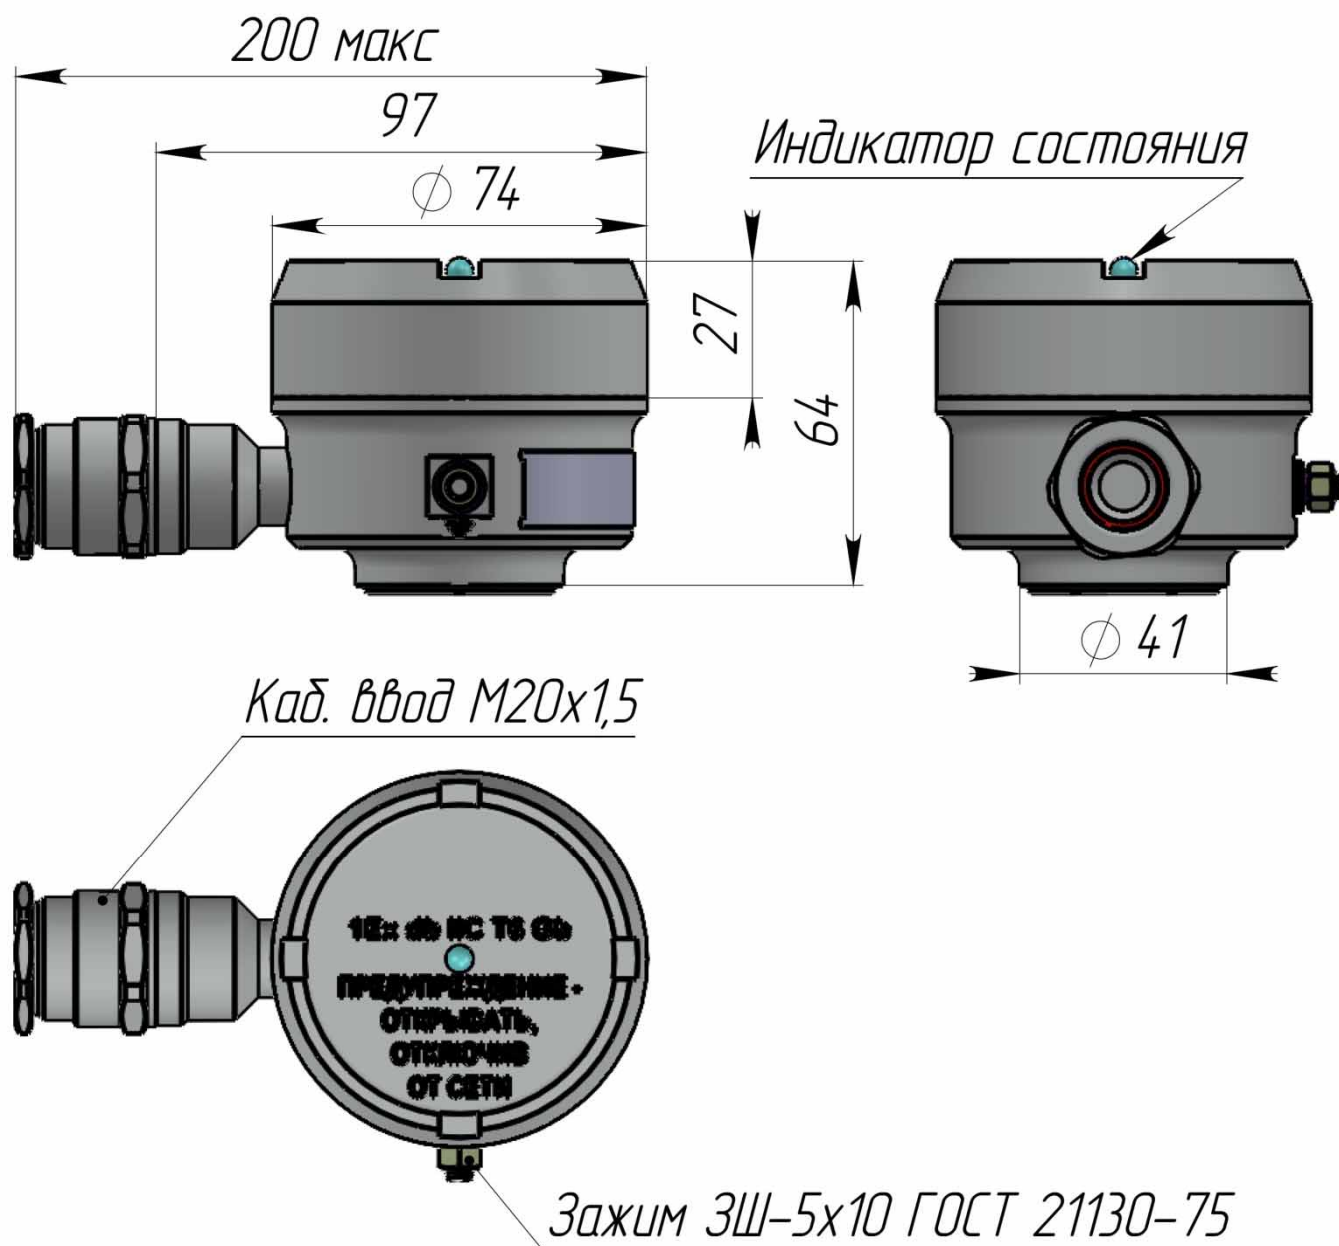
Габаритные размеры корпуса блока электронного в корпусе из нержавеющей стали для оборудования класса безопасности ЗН
